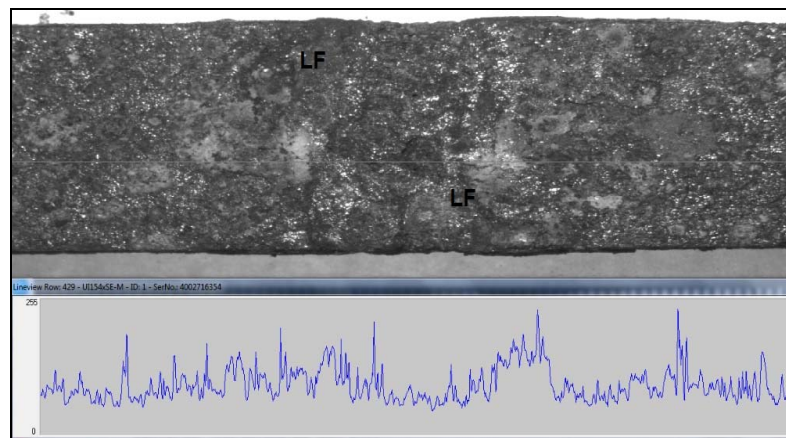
Superficie de la probeta con soldadura MMA a tensión.
